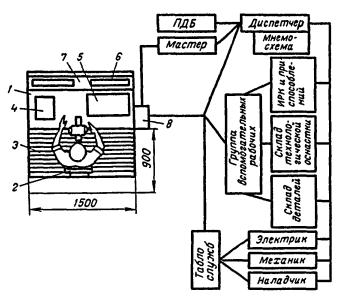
Планировка рабочего места слесаря: l — верстак слесарный; 2 — стул подъемноповоротный; 3 — решетка под ноги; 4 —
